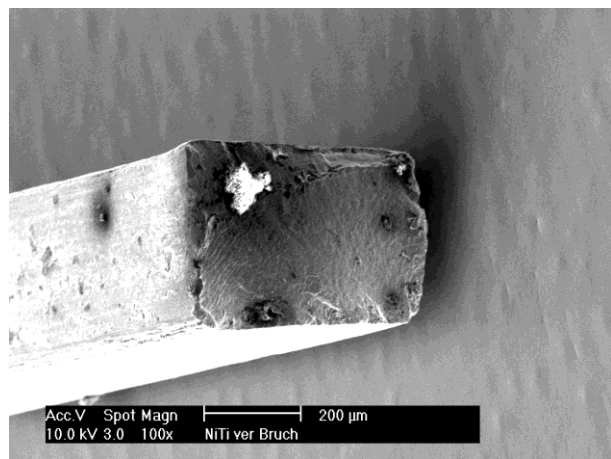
Beta Low Friction-Draht, Bruchstelle und Rand (100-fach vergrößert)
